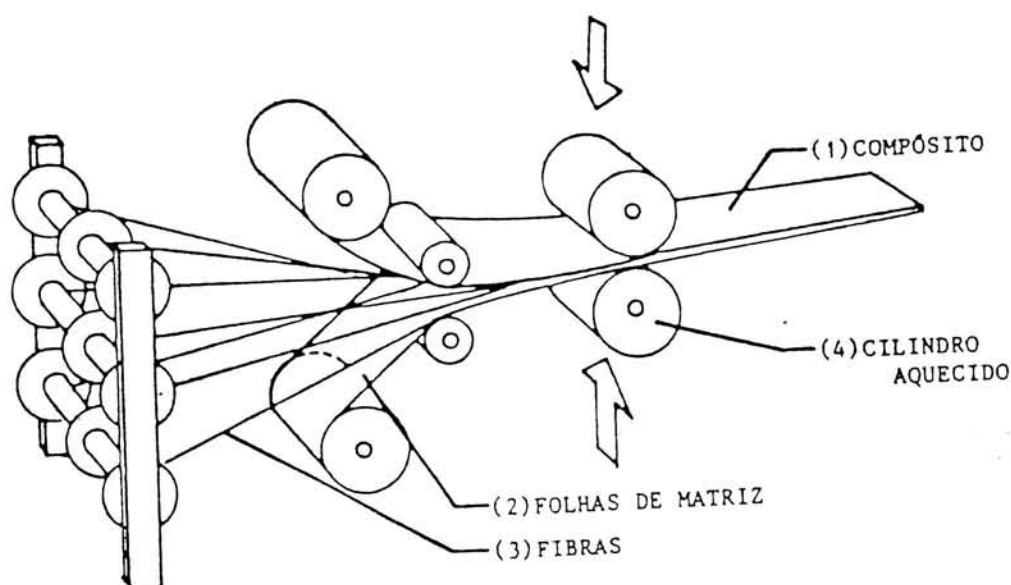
Esquema de fabricação de compósitos por colaminagem [9]
